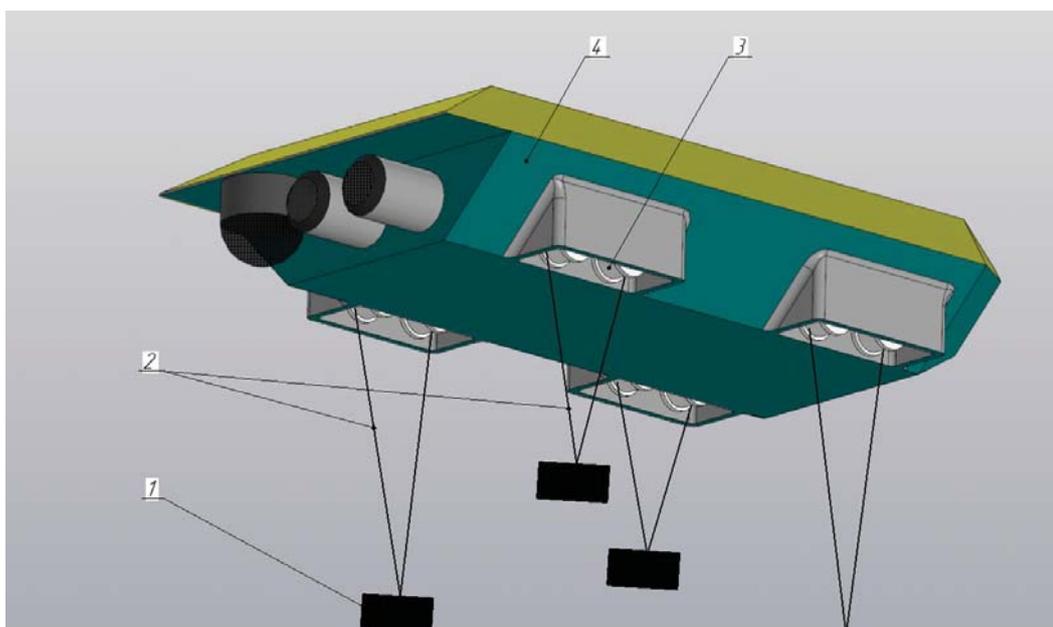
Общий вид и устройство платформы с якорно-тросовым движителем:
